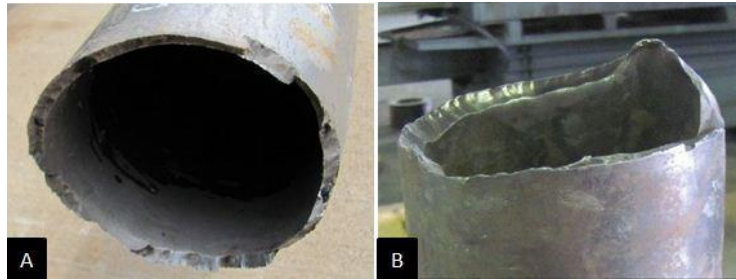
Поверхня руйнування бурильних труб, корпус 1 (А) і корпус 2 (В)
